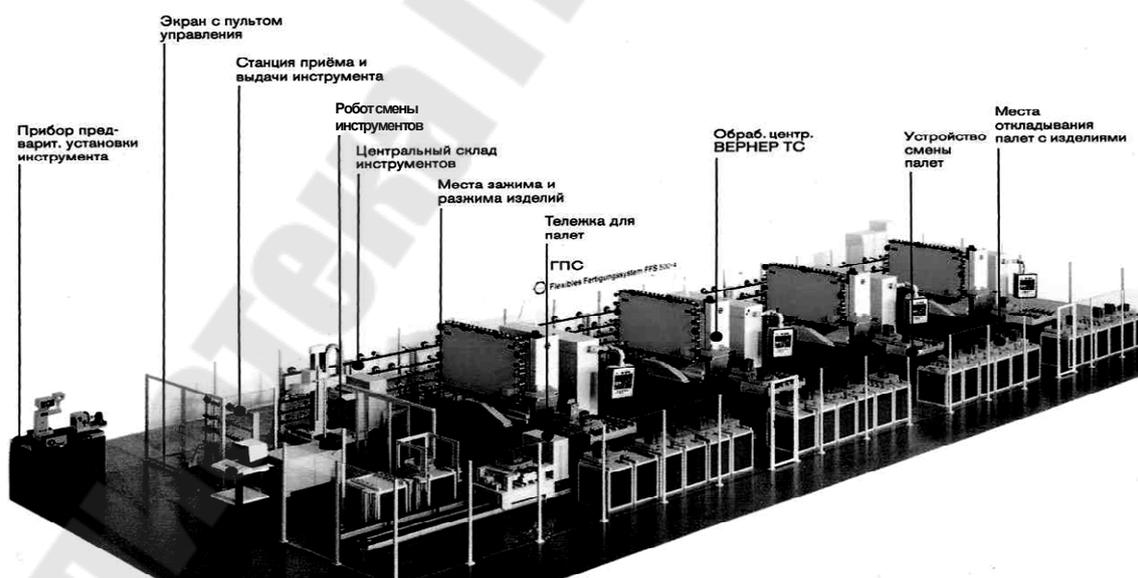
Управляемая с помощью ЭВМ гибкая производственная ячейка «ГПС500-4» фирмы «Вернер» с четырьмя обрабатывающими центрами и автоматическим снабжением заготовками и инструментами
